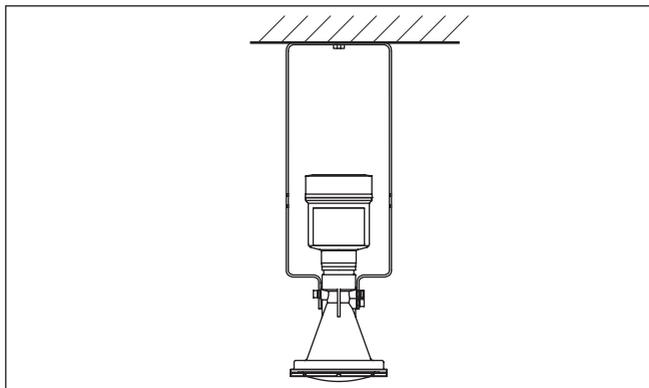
Montaggio sul cielo tramite la staffa di montaggio lunga 300 mm
